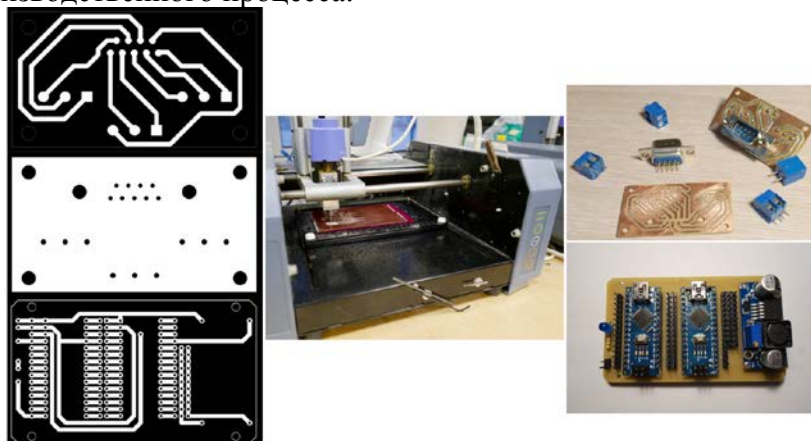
Изготовление печатной платы на прецизионном фрезерном станке
